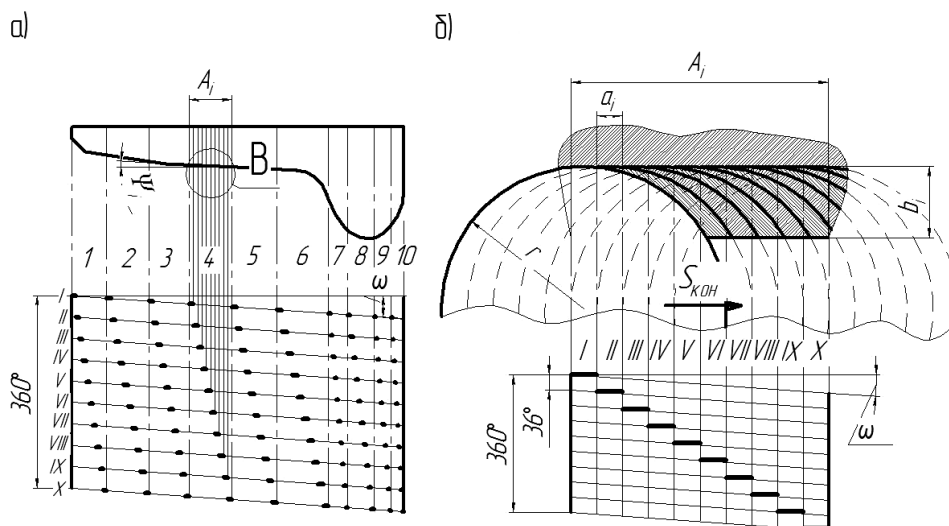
Схема фрезерования профиля колеса на развертке и в основной плоскости:
